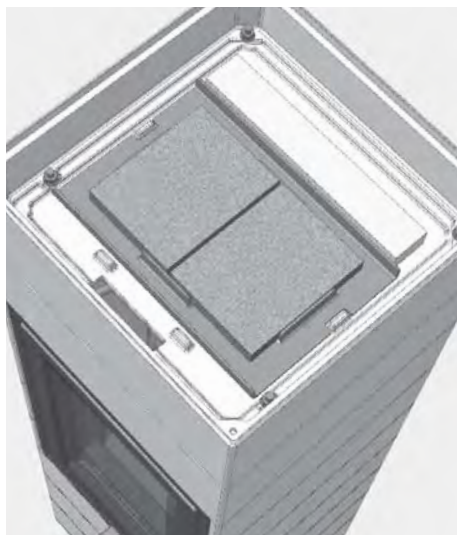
Position des plaques du catalyseur sur le CORNA tec, vue de dessus sur la plaque de recouvrement démontée
